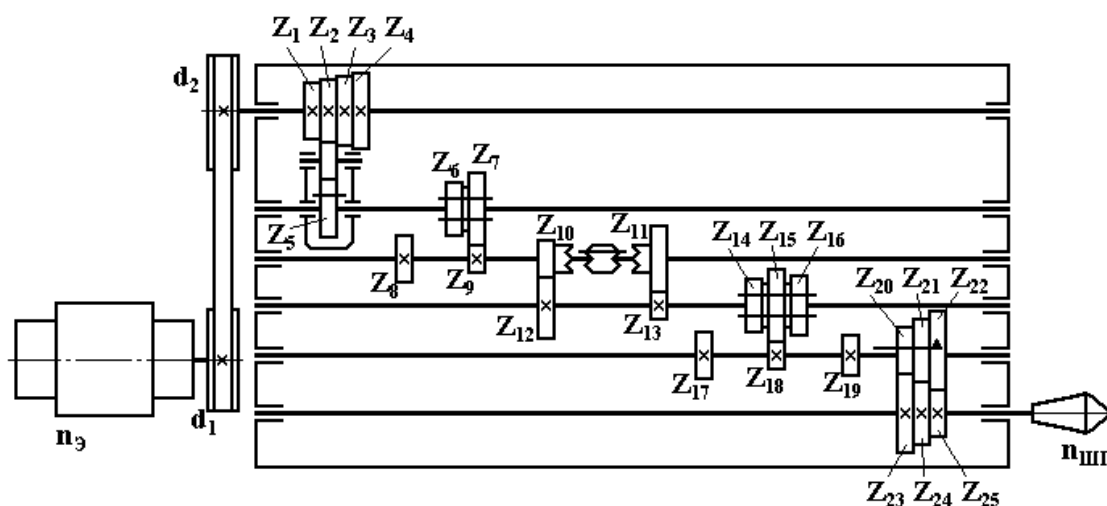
Кинематическая цепь главного движения условного станка (вариант № 19)
